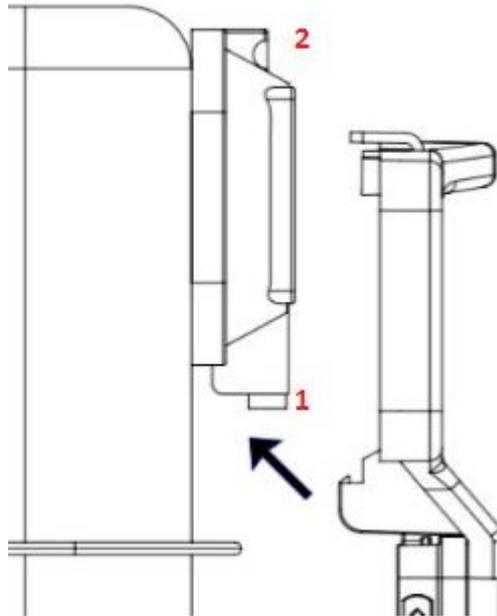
El método de enrutamiento del cable transmisor de pulso - ensamblaje superior
